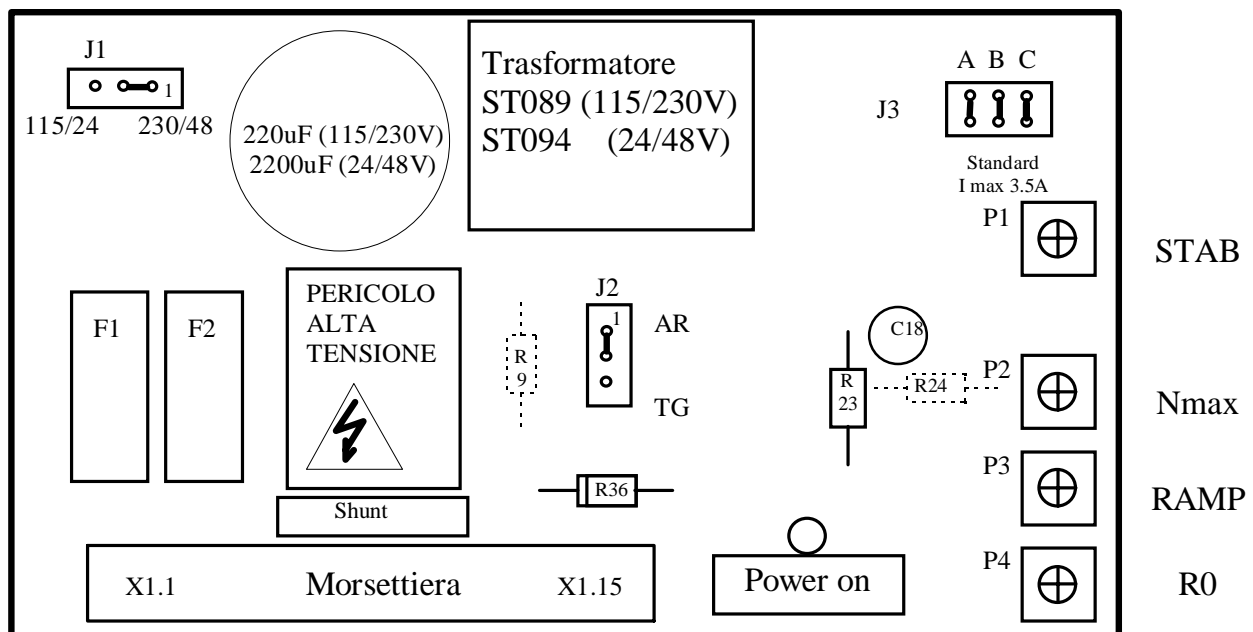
Layout scheda: posizione standard di jumper, trimmer e componenti su torretta
